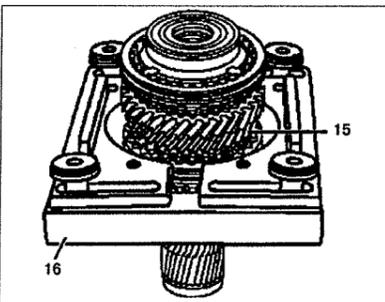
Ведущий вал (автомобили с двигателем 611.980):
